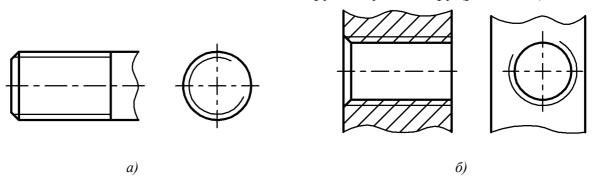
Изображение резьбы на чертежах: a — на стержне; δ — в отверстии
